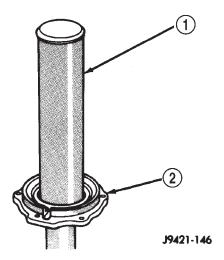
JUNTA DE ENGRASE DE RETENEDOR DE COJINETE
